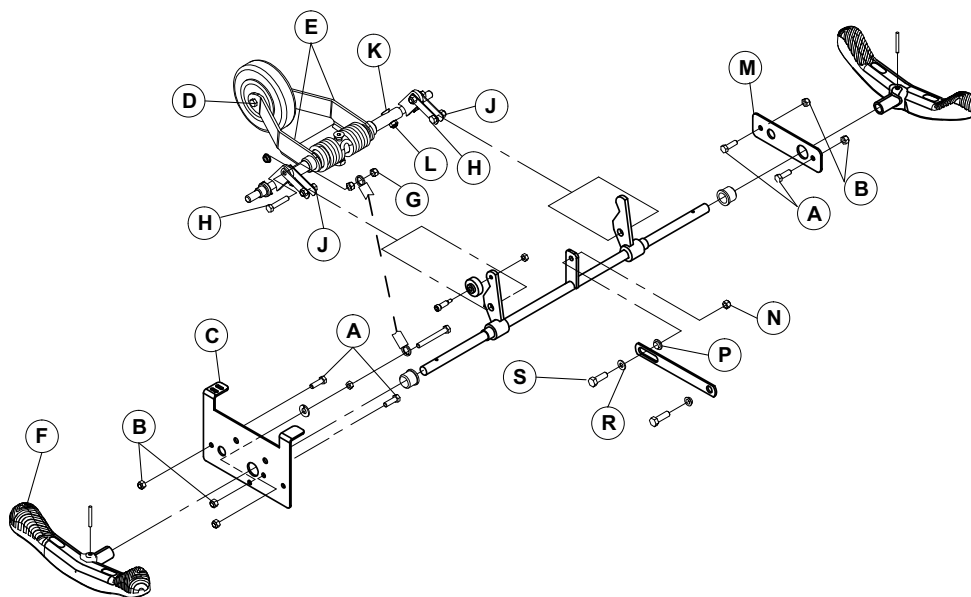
Remplacement de l'ensemble de bras de cinquième roue, base hydraulique
